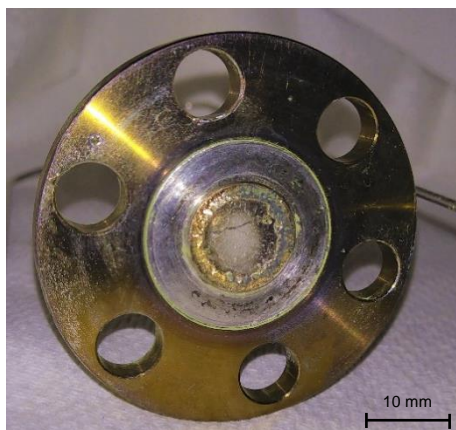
Photo du fritté de la boucle SoIO fixé à l'obturateur par soudure à l'or et au platine.
